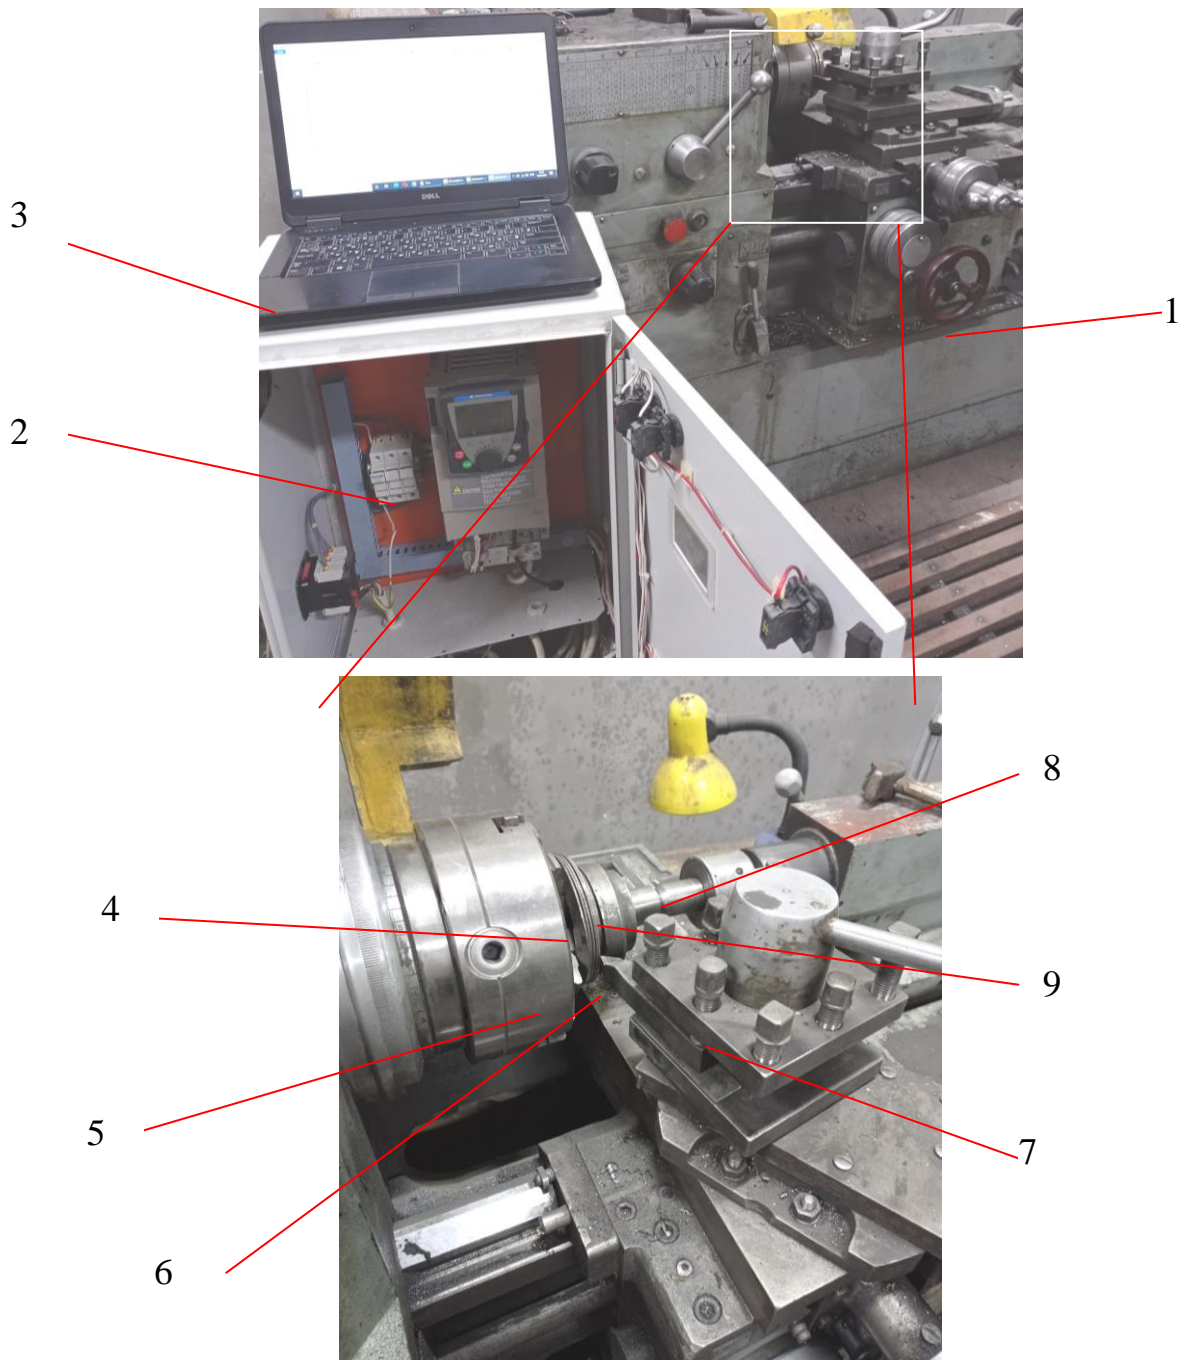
Процес проточування витків заготовки гвинтового секційного робочого органу на токарно-гвинторізному верстаті:
